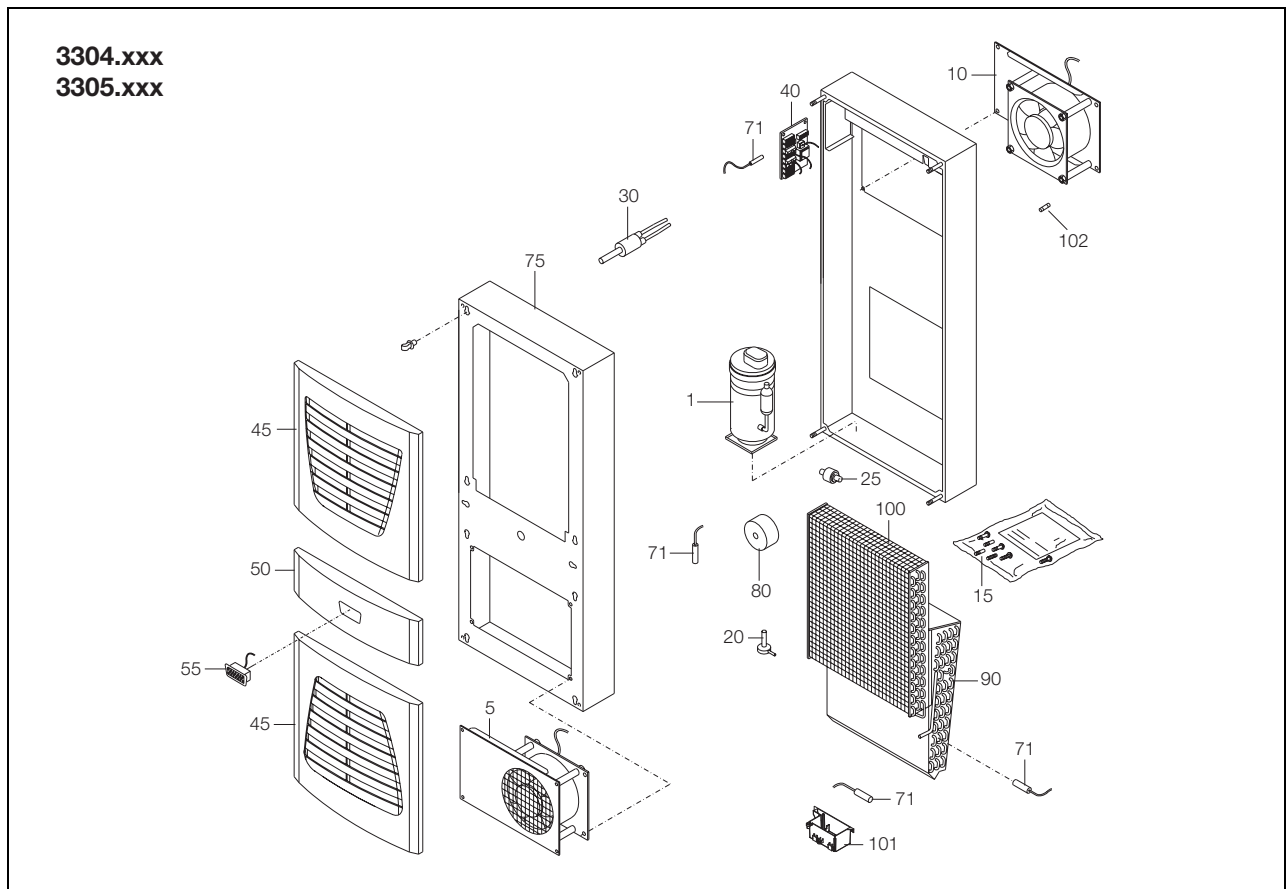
Pièces de rechange 3304.xxx, 3305.xxx
